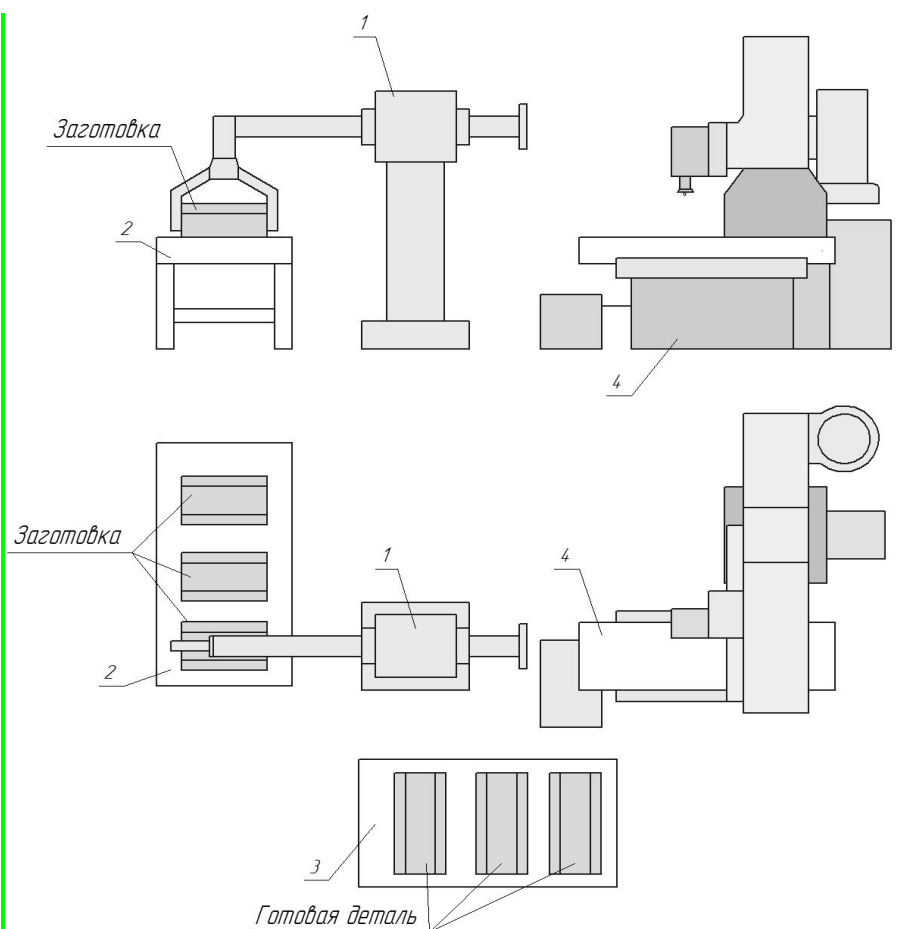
Роботизированный участок модернизированного плоскошлифовального станка 3E711B
